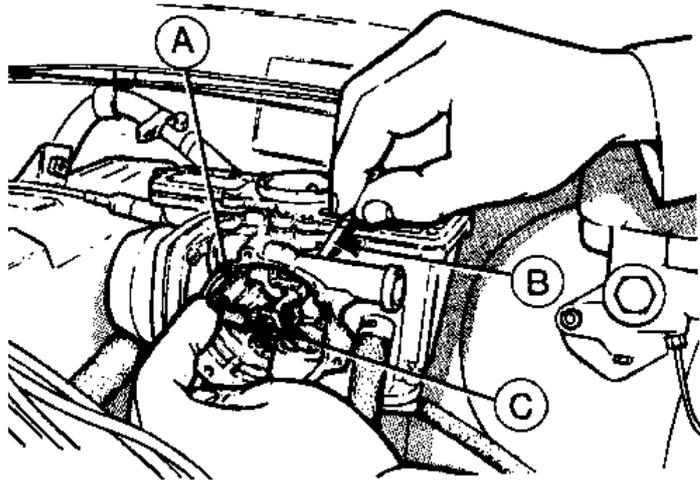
Рычажок привода автоматической воздушной заслонки (А), сверло (В) и гайка (С) (Разд.25)
